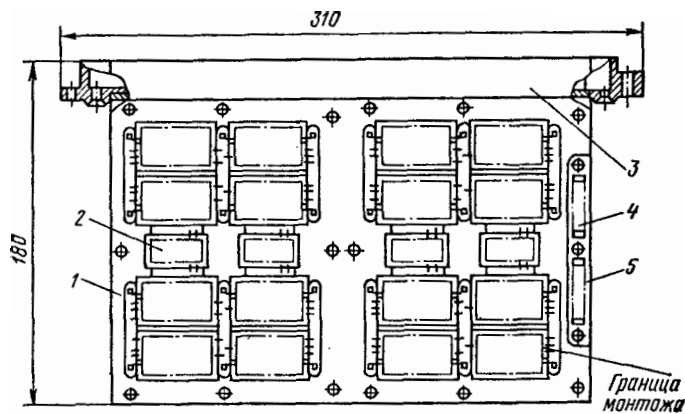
Рамочная ячейка герметичного блока РЭА книжной конструкции с воздуховодом:
